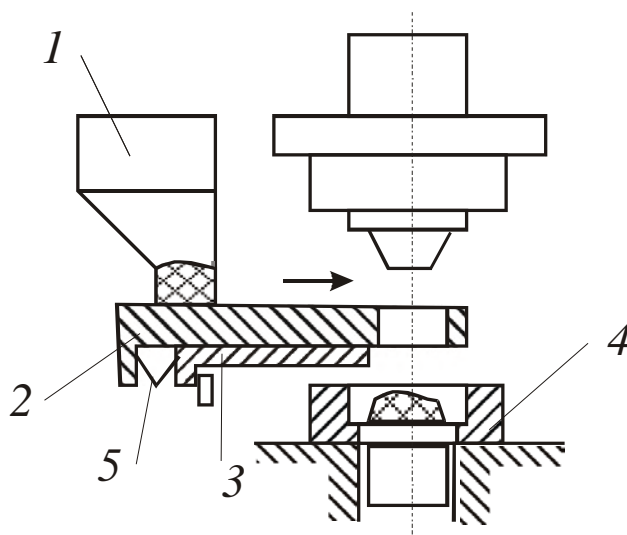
Устройство для загрузки пресс-порошка в пресс-автомат:
